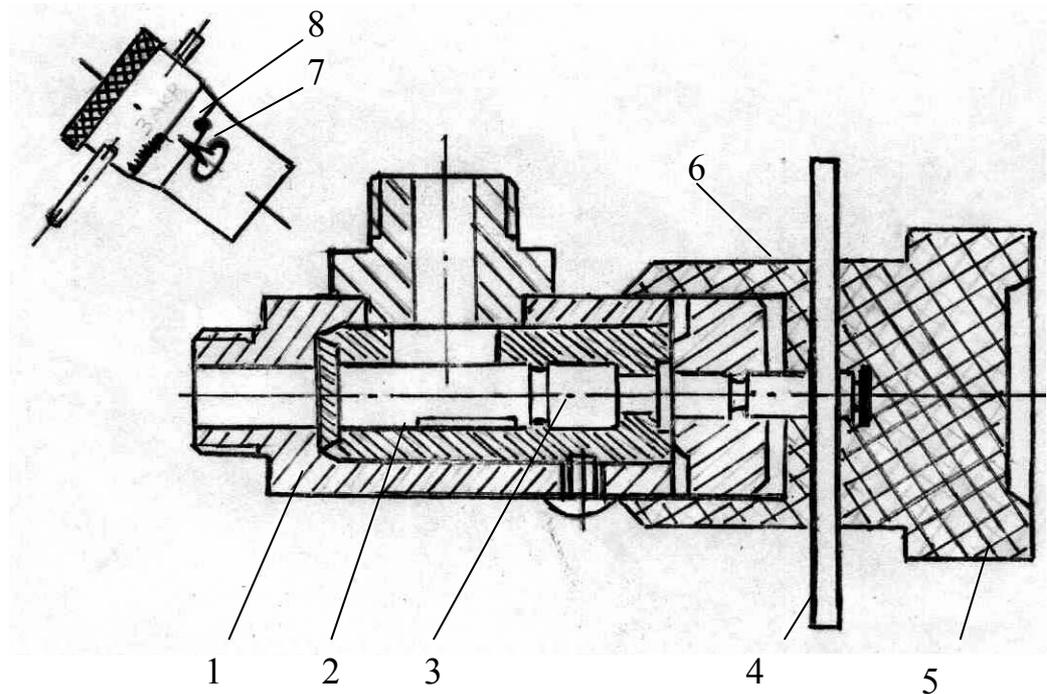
Схема устройства прибора ДР-70 (КИ 1097)
